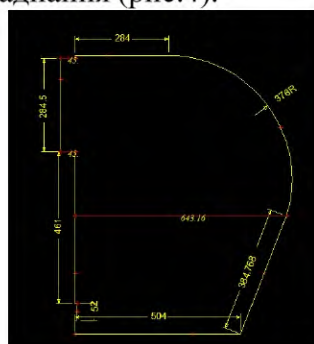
Приклад робочого креслення для виготовлення кронштейна на плазморіжучому обладнанні
